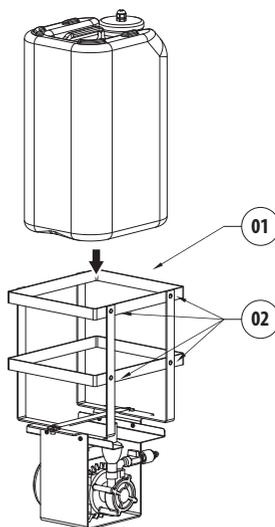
Réservoir 23l, hauteur de remontée d'eau de 30m.
